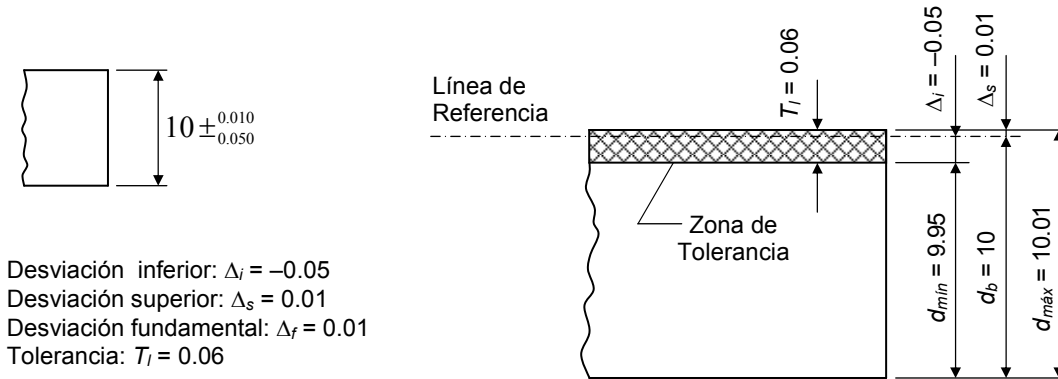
Ejemplo de una pieza de 10 mm de altura, con tolerancia bilateral (todas las medidas en mm)
